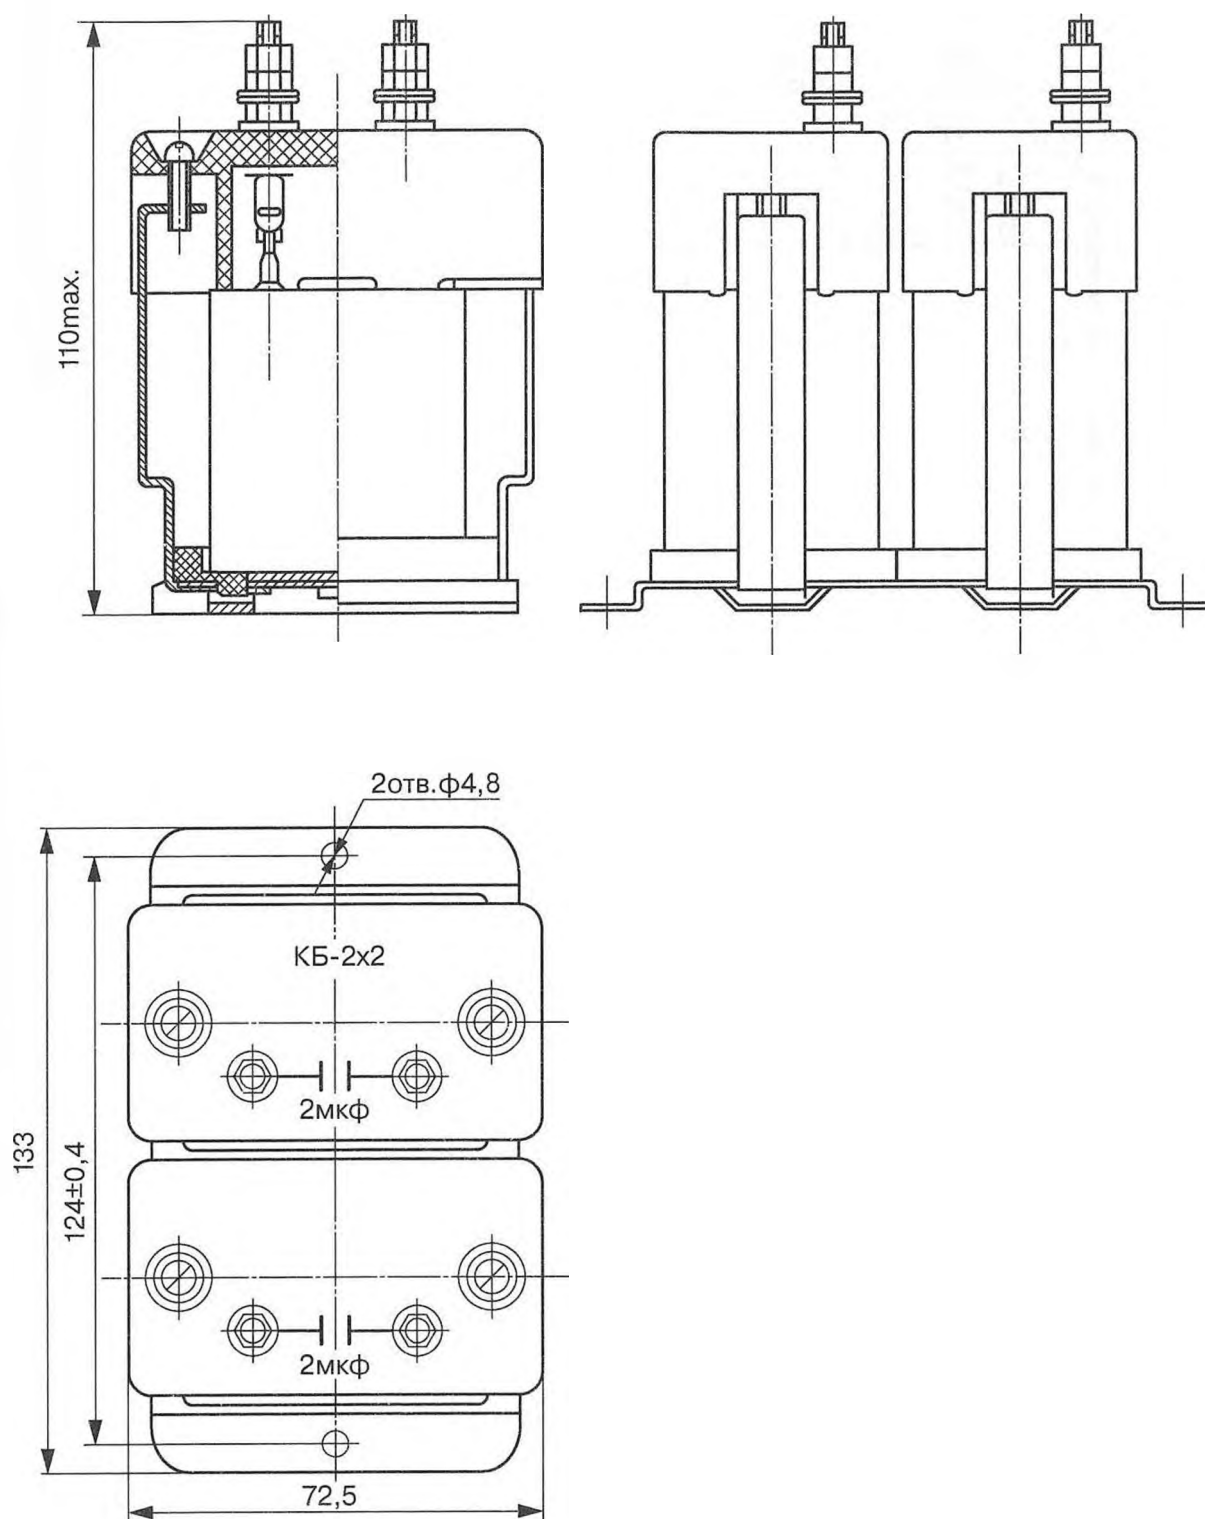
Габаритные и установочные размеры блока конденсаторного KB-2x2
